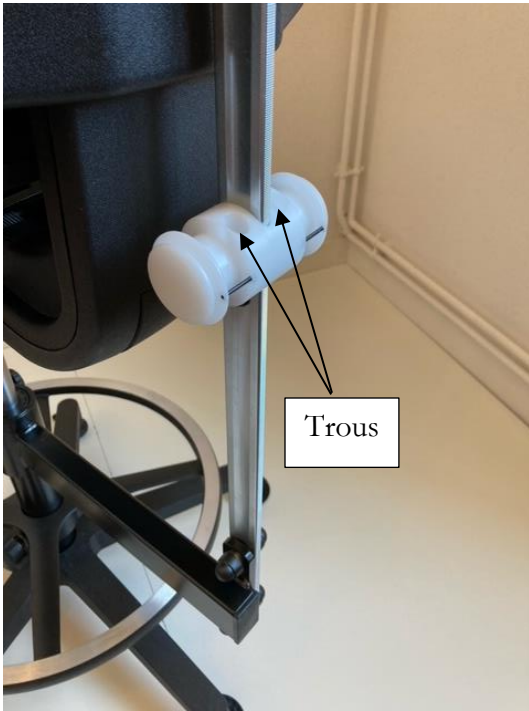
glisser le tambour, les deux trous vers l'arrière.
